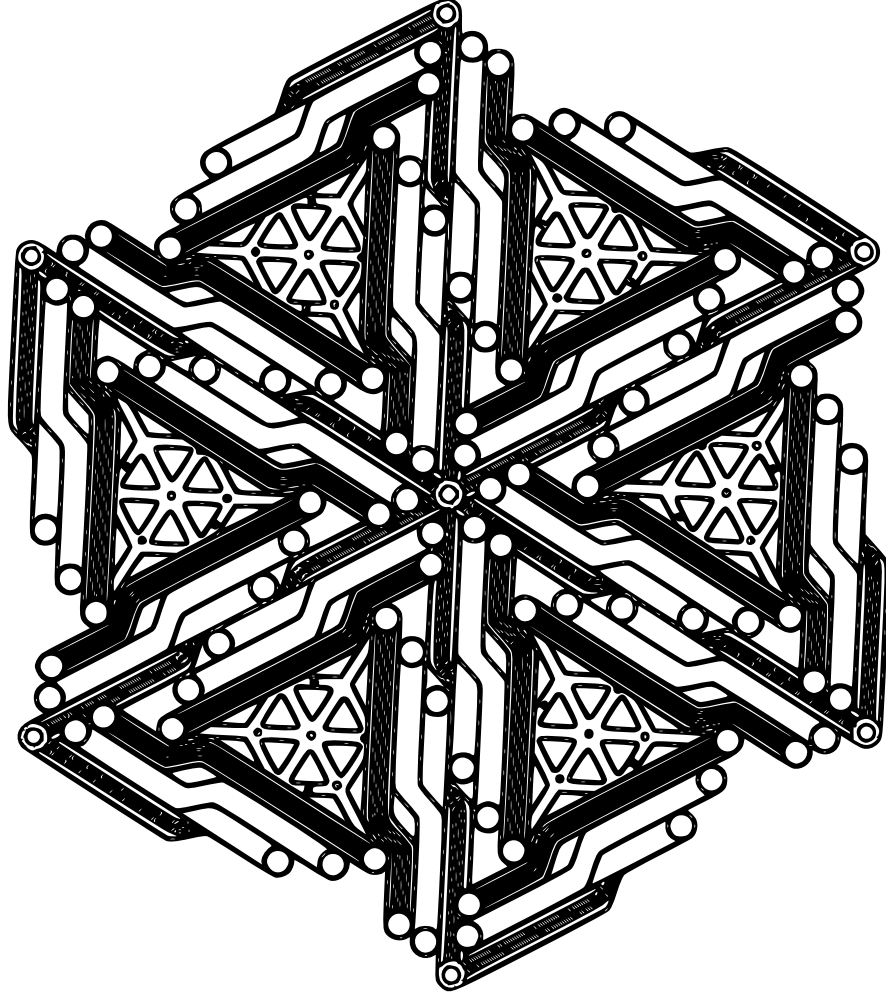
Assemblage plan de six mécanismes triangulaires entraînés par courroies.
